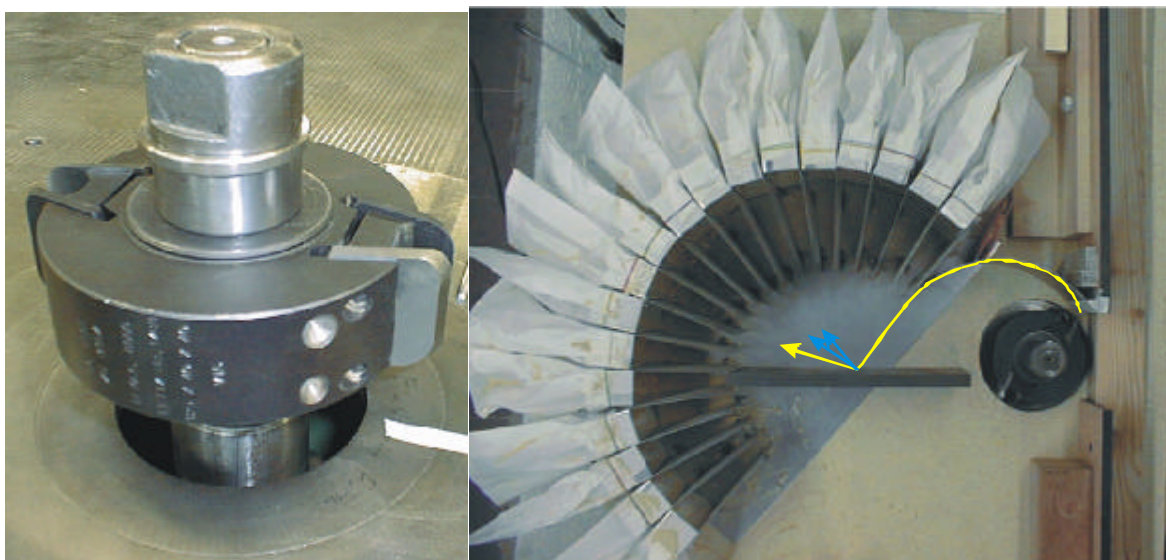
Werkzeug (links), Versuchsaufbau (rechts)
